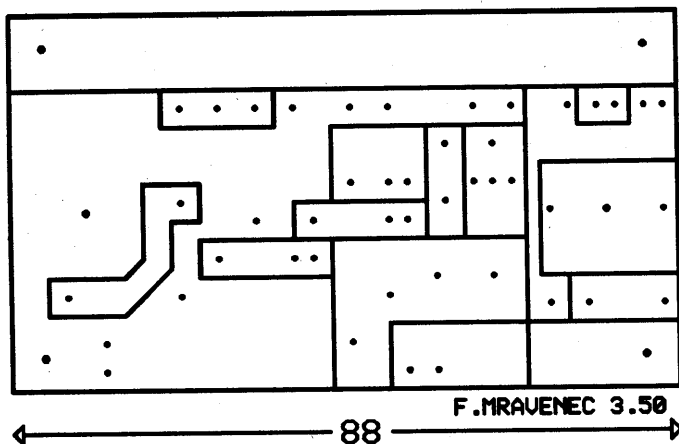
Zapojení vř zesilovače a detektoru pro SV a DV
